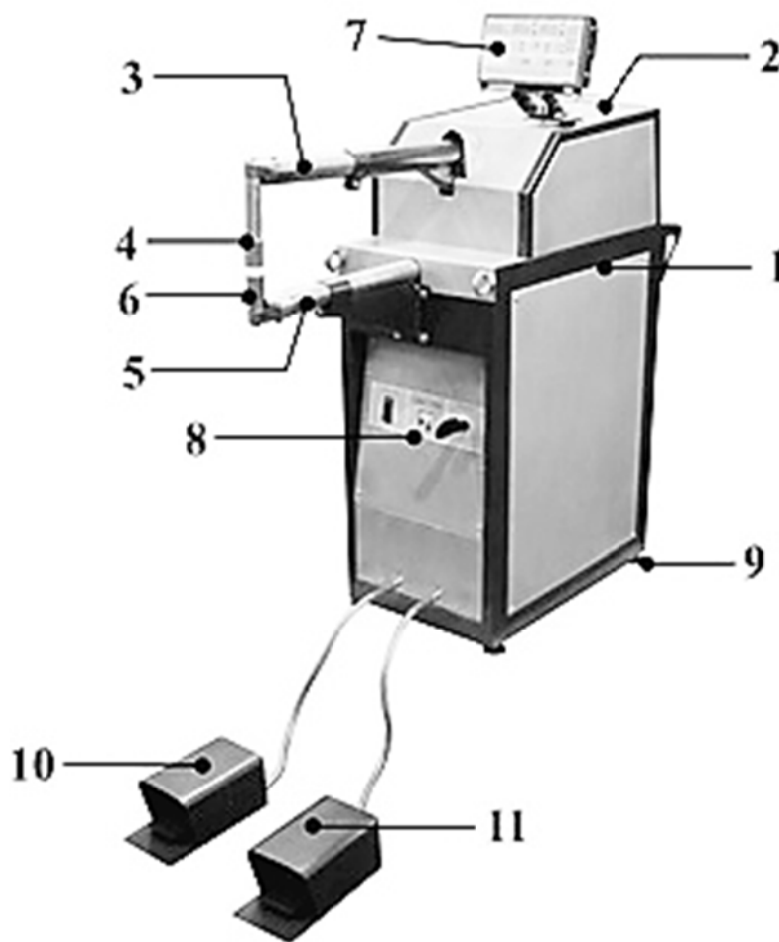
Внешний вид машины для контактной точечной сварки
